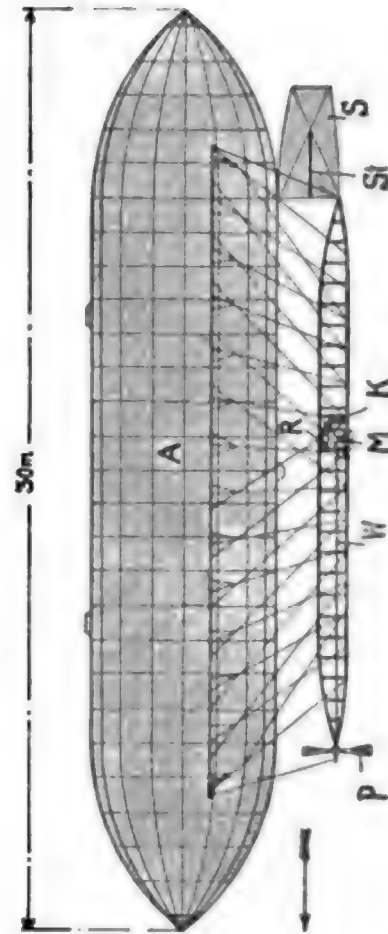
Zeichnung des Luftschiffes der Gebrüder Renner, Seitenansicht. A Ballon, S Seitensteuer mit seitlichen Stabilisierungsflächen St, M Motor, K Kühler, R Benzinhälter, H' Antriebswelle für den Propeller P.
